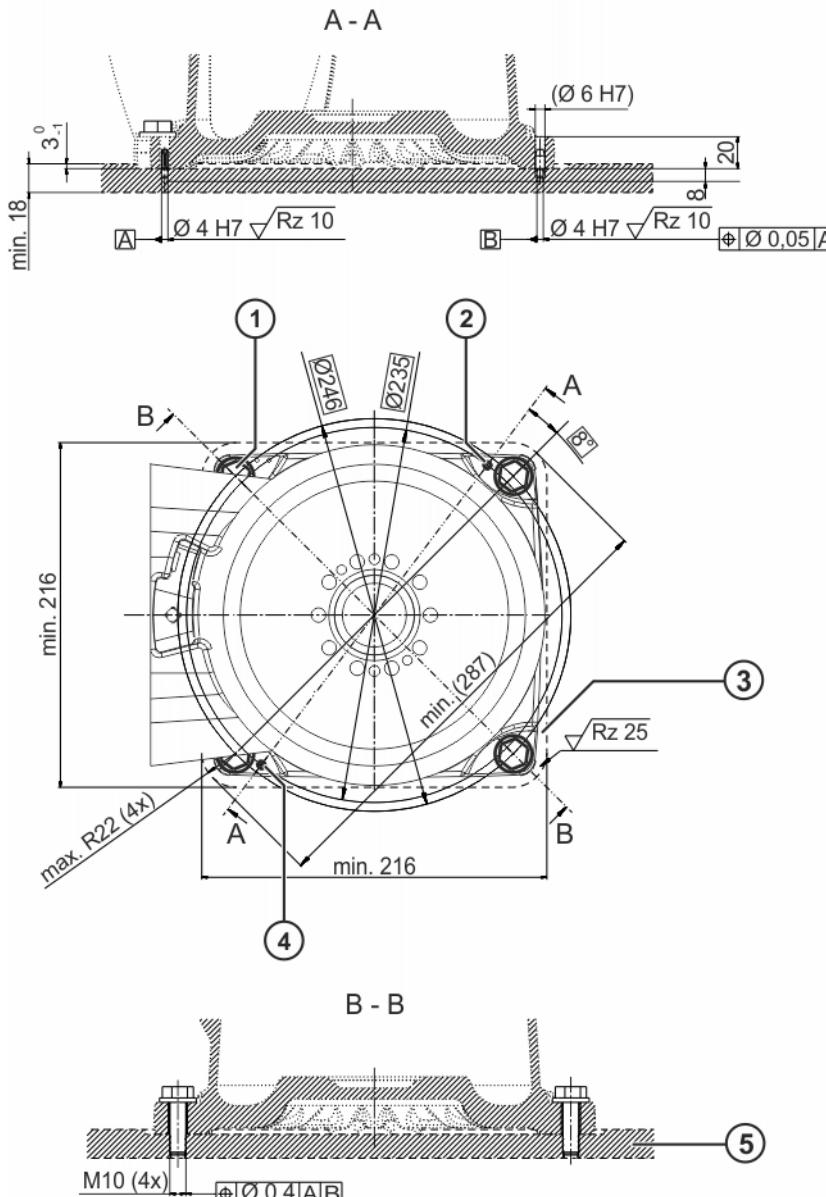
Maschinengestellbefestigung, Maßzeichnung
